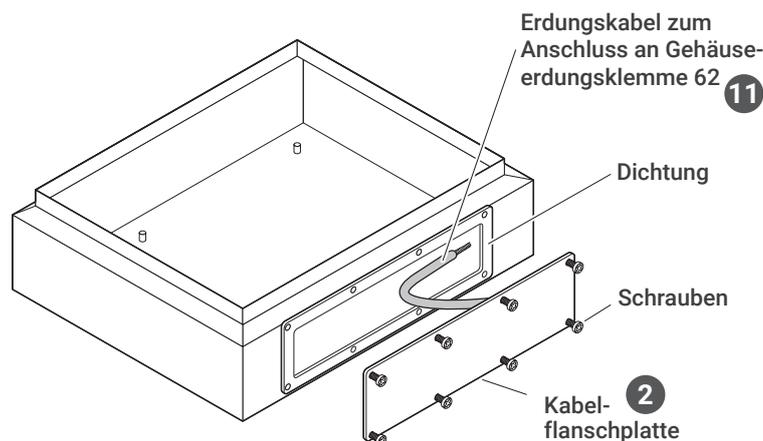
Abnehmbare Kabelflanschplatte
